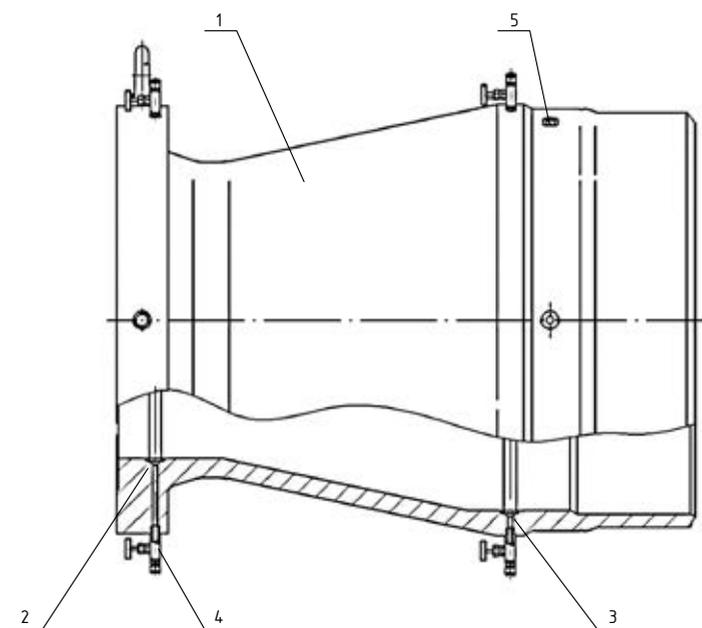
Конфузор компрессора: 1 – корпус в сборе; 2, 3 – обечайка из трех частей; 4 – клапан игольчатый; 5 – пробка
